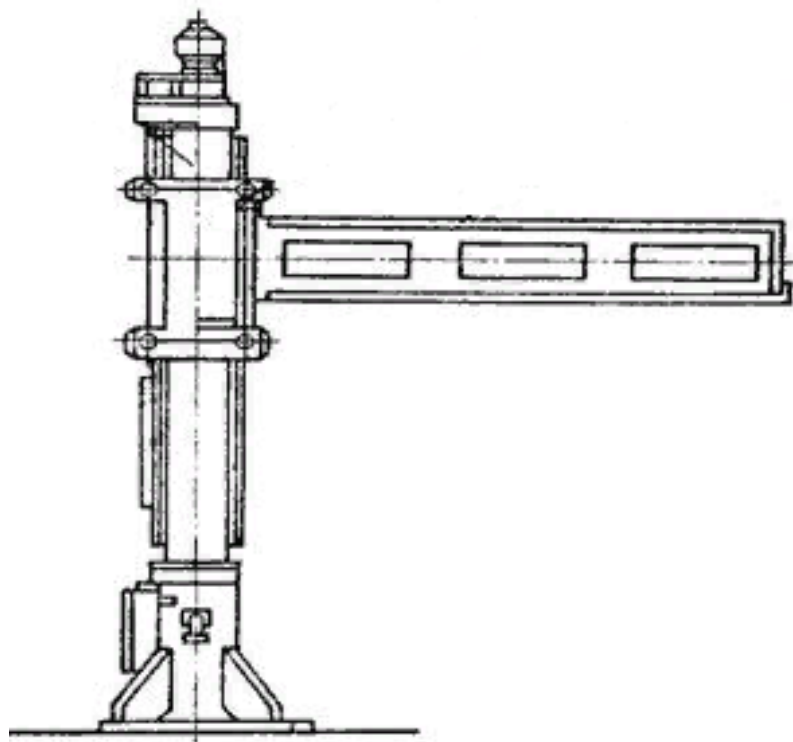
Колонна сварочная поворотная ПК-2
